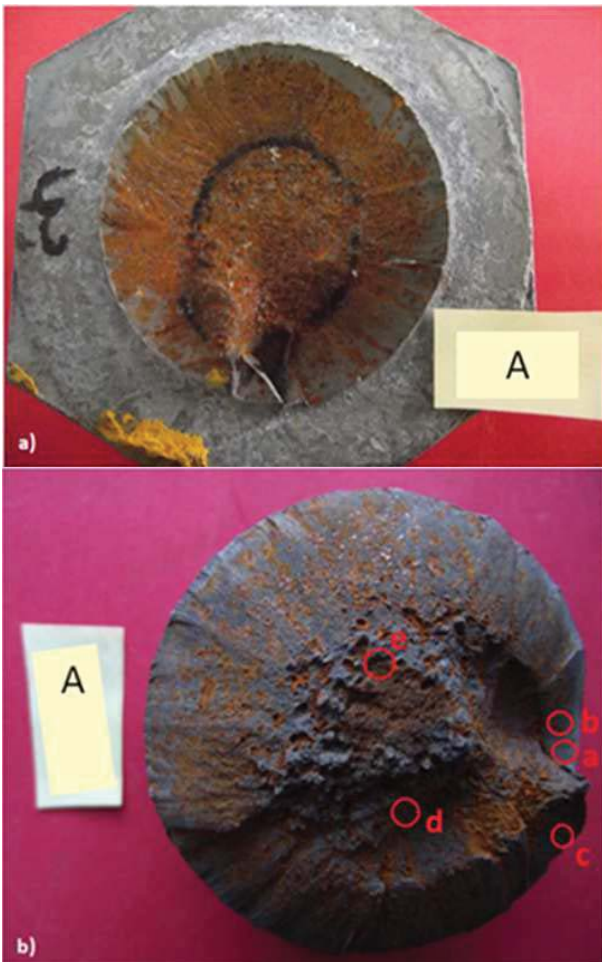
Superficies de fractura del perno A. a) cabeza; b) fuste.
